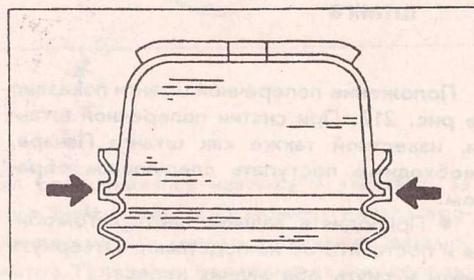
Установка колпака на защитный кожух. Детали (8) и (10) показаны на рис. 217.
